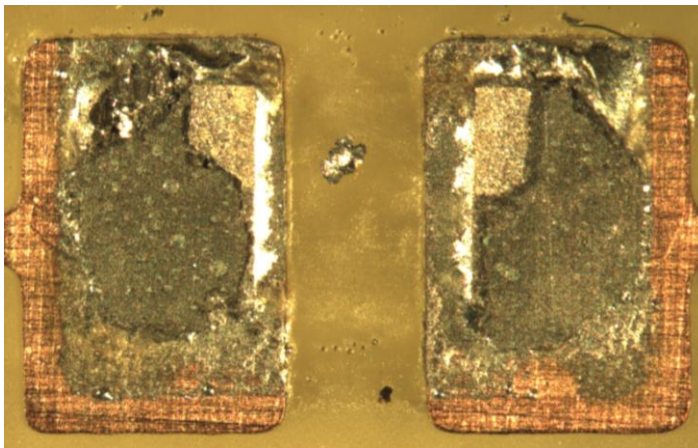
Kontrolní měření s hlavou v kontaktu s deskou
